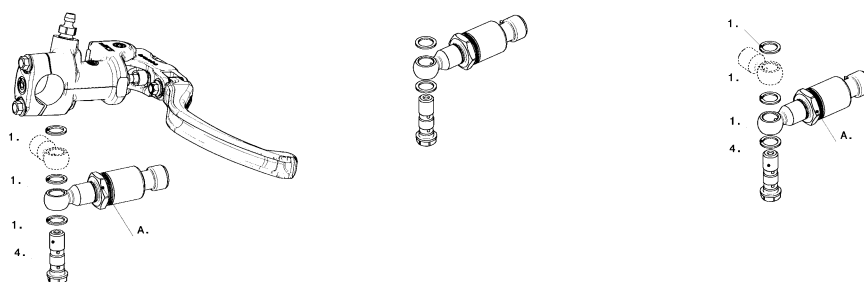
Montaje del sensor de presión en el cilindro maestro del freno
